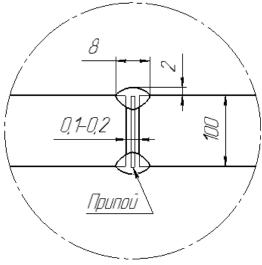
Кольцевой шов для сварки частей в целях создания местной герметизации паяного шва
